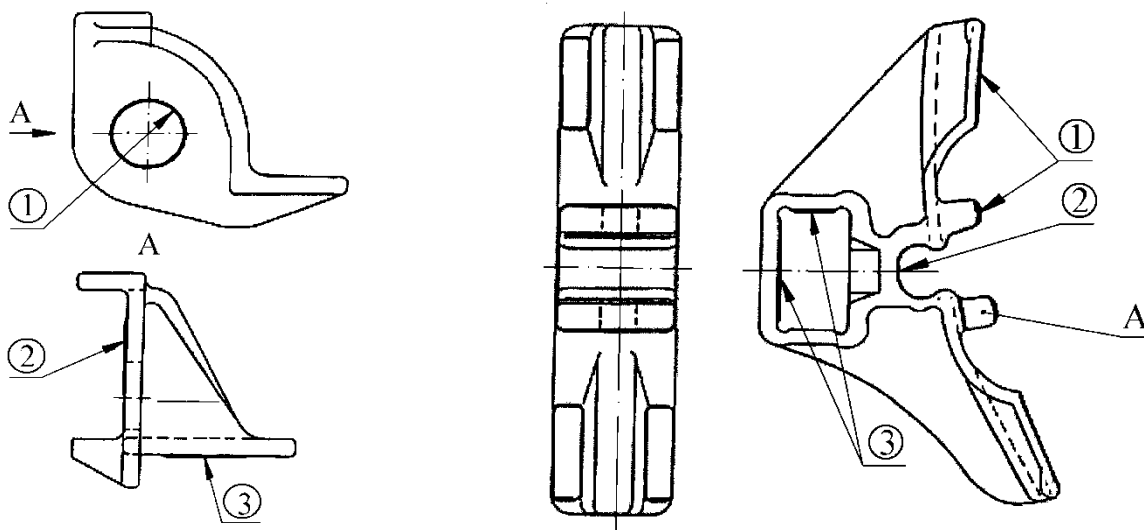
Наконечник триангеля    Рисунок 8.26 - Башмак неповоротный
